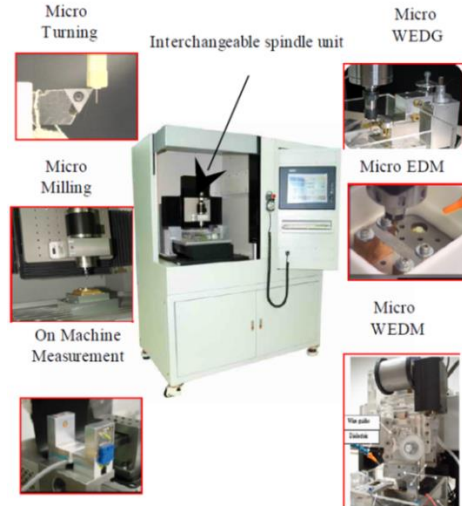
Machine usinage hybride DT-100 d'après [65].
